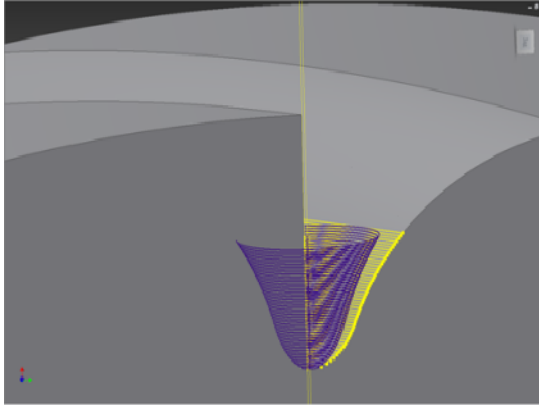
Поверхность профильной фрезы для обработки выходной детали
